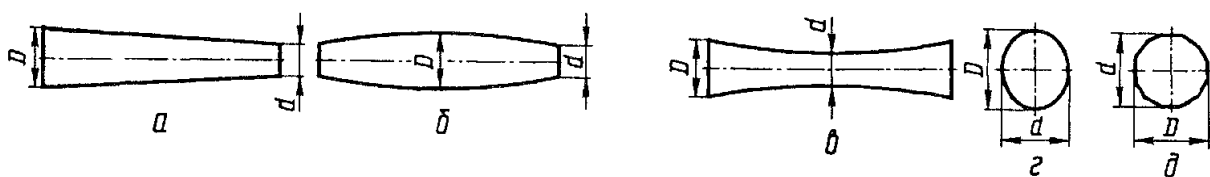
Похибки форми циліндричних поверхонь:
